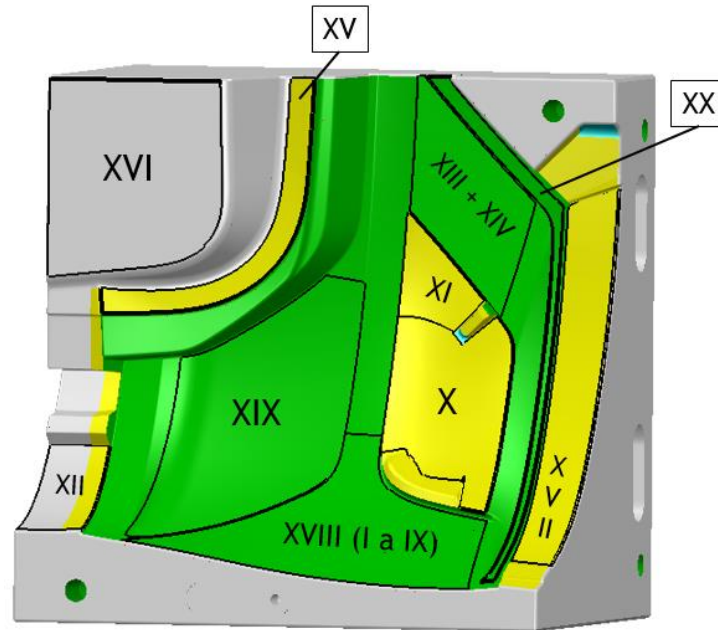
Modelo CAD do molde exemplo e zonas de teste.
